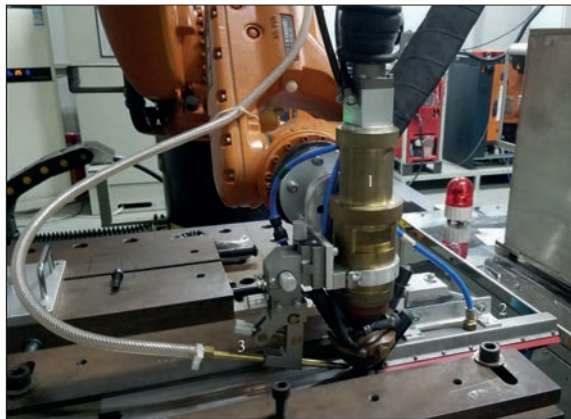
Внешний вид головки для лазерно-микроплазменной сварки в руке робота KUKA KR30HA: 1 – интегрированный плазмотрон; 2 – система защиты формируемого шва; 3 – мундштук для подачи присадочной проволоки
